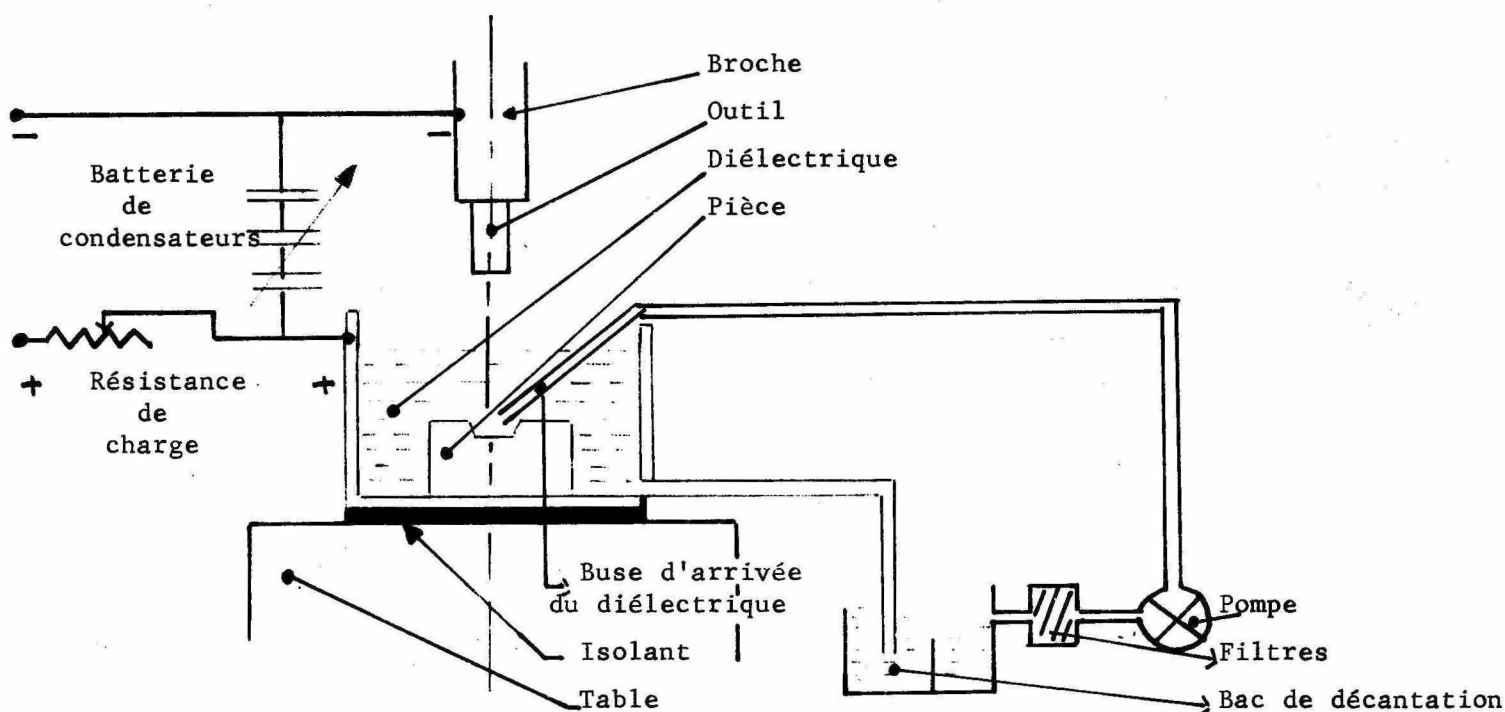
Principe d'une machine d'usinage par Electro-Erosion
